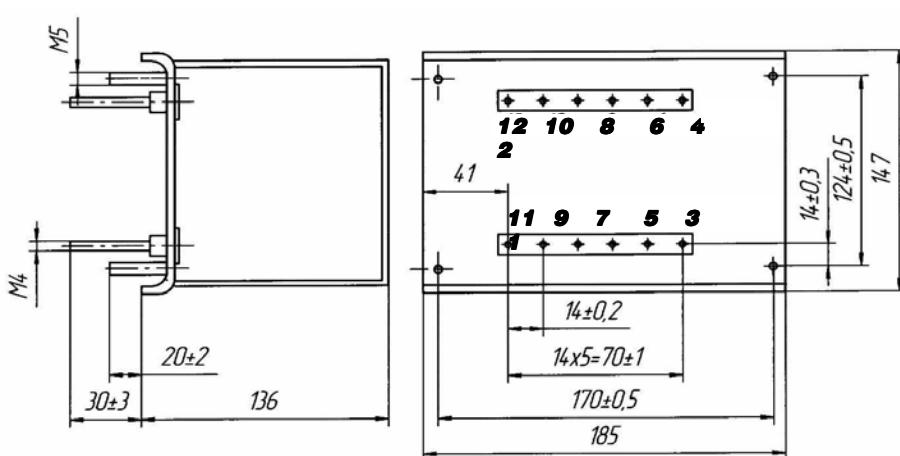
Габаритные, установочные и присоединительные размеры приставки типа ПТ-1.
